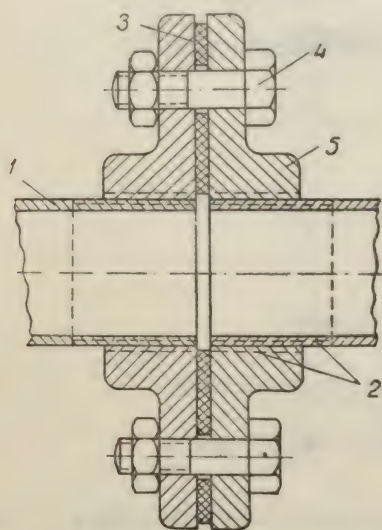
Соединение труб при помощи фланцев на резьбе:
